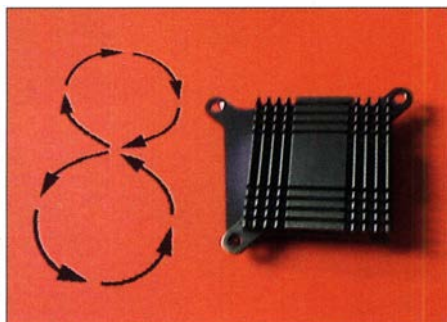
Ausgangsposition zur Bearbeitung der Kühlkörper Fotos: Preen
